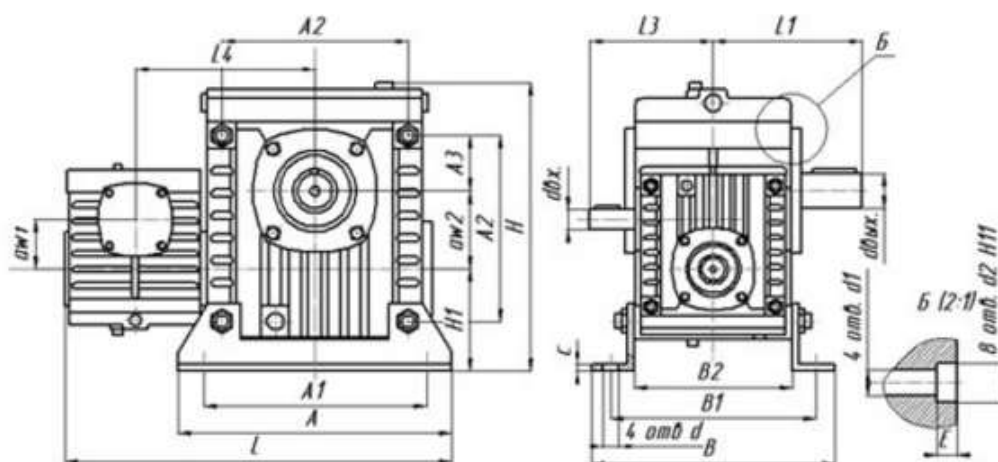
Габаритные и присоединительные размеры редукторов Ч2-40/63
